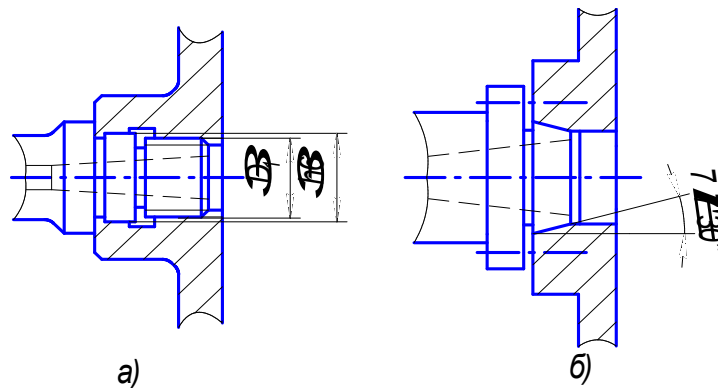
Способы центрирования и крепления приспособлений на шпинделе токарного станка
